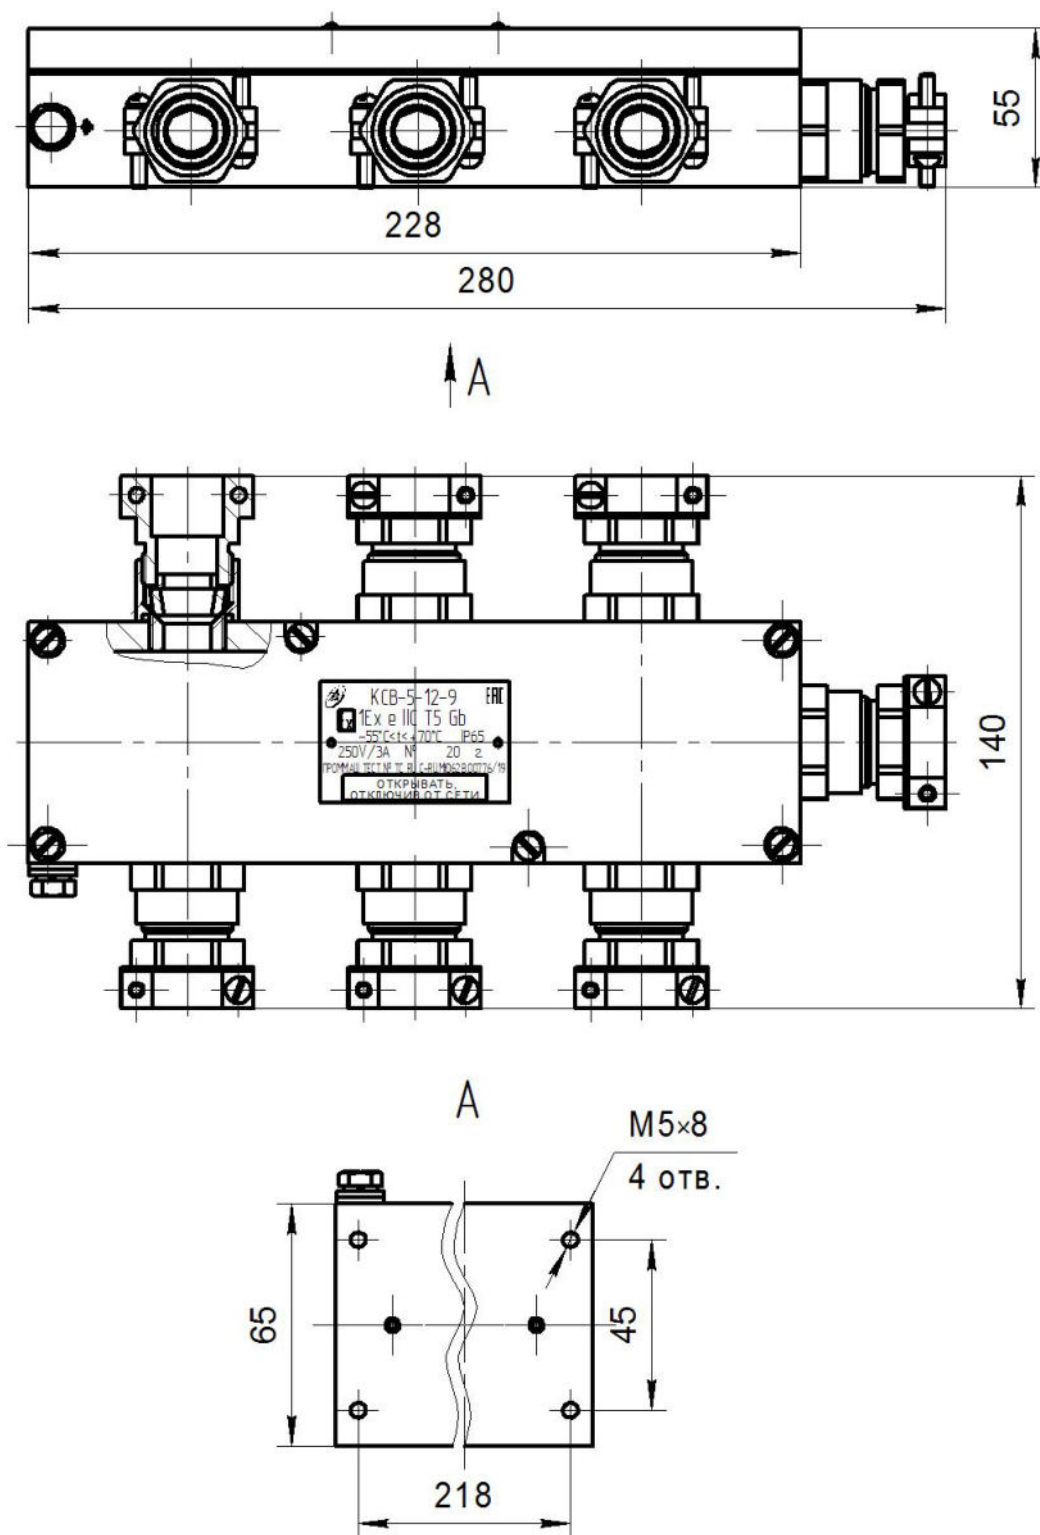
Внешний вид и присоединительные размеры коробок:
